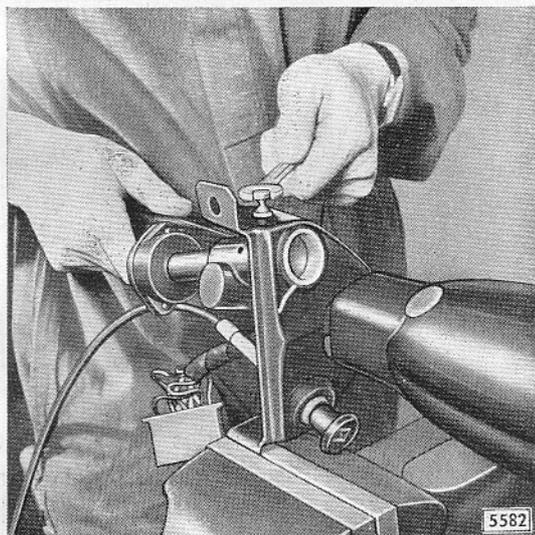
Lenk- und Zündschloß am Lenkstützrohrhalter mit Abreißschraube befestigen
